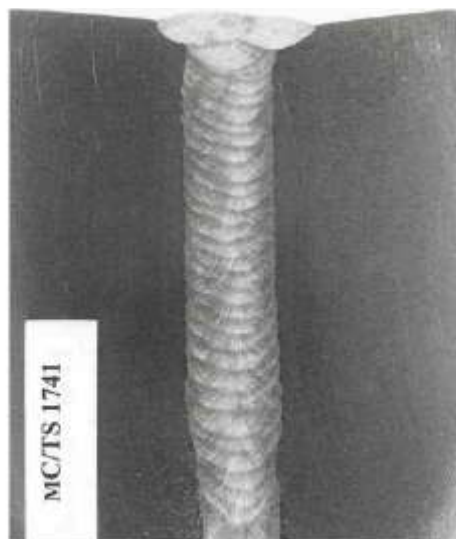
Фотография шлифа шва открытого для всех участников образца после сварки и до зачистки поверхности (по данным TRUEFLAW). Показана форма разделки шва и структура многопроходного заполнения шва.
